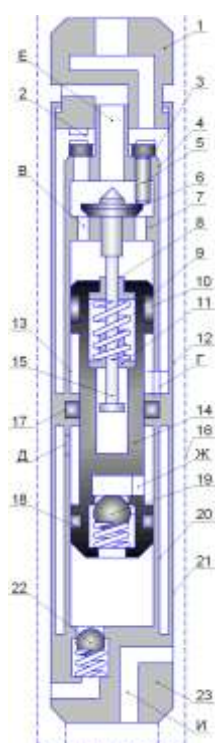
Схема ППН конструкции Неудачина Г.И. и Пилипца В.И.
